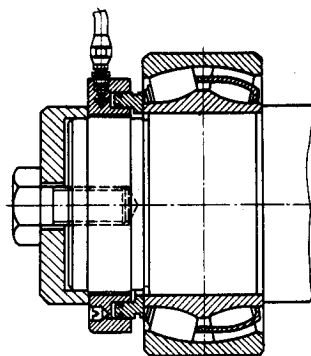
Установка крупных подшипников с помощью гидравлической гайки
